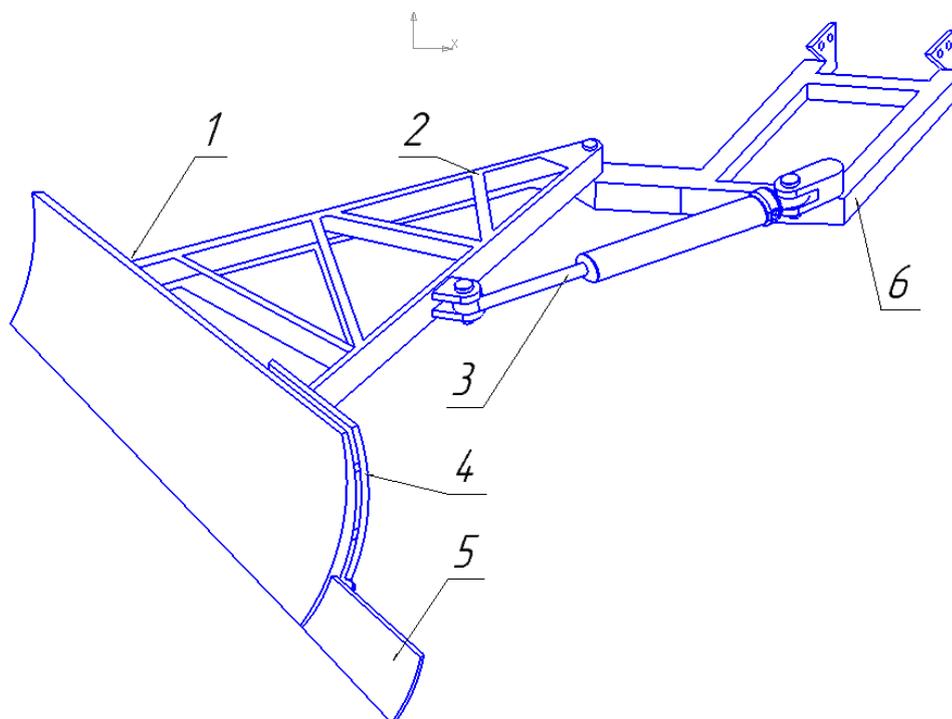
Рабочий орган снегоуборочной машины: 1 – отвал, 2 – рама поворотная, 3 – гидроцилиндр, 4 – выдвжной открьлок, 5 – поворотный открьлок, 6 – рама неповоротная
